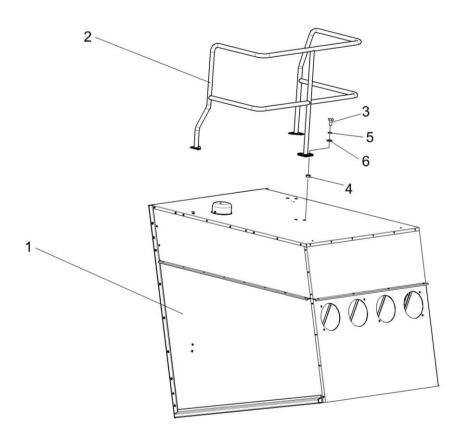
Установка капота КЗК-8А-0228100-03
